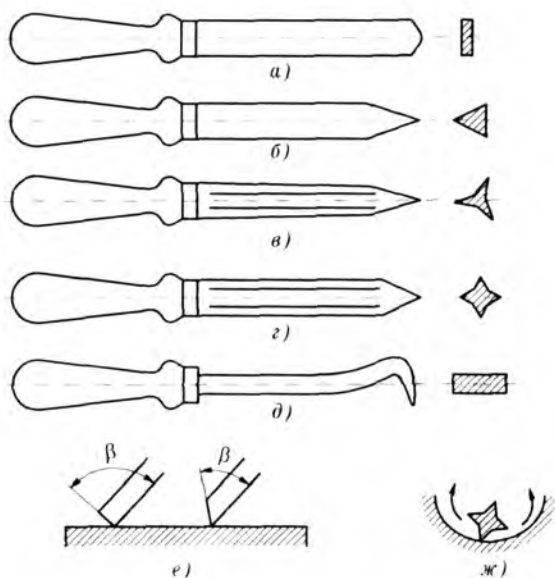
Виды шаберов, форма режущей части и обработка цилиндрической поверхности:
